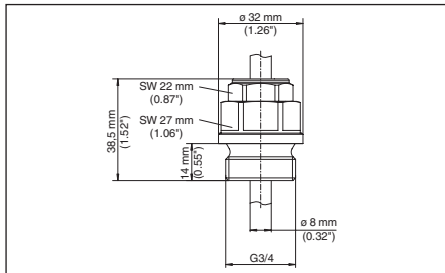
Atornillamiento de cable de suspensión G $\frac{3}{4}$  (DIN 3852-A)
